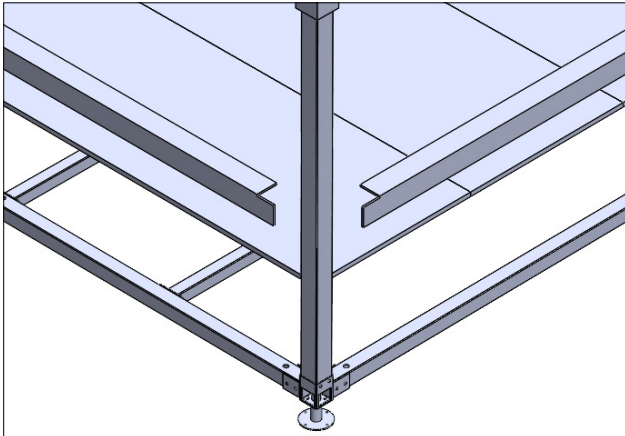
Vista del stand modelado en Solidworks, apreciando las paredes de "mimbre".
